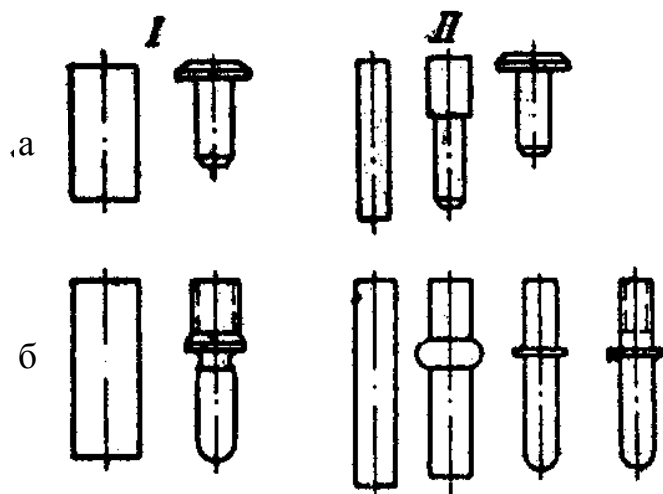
Приклади заміни обробки з зняттям стружки обробкою тиском - холодною висадкою - при виготовленні двох контактних деталей а, б. I - обробка на металорізальних верстатах; II - холодна висадка.
